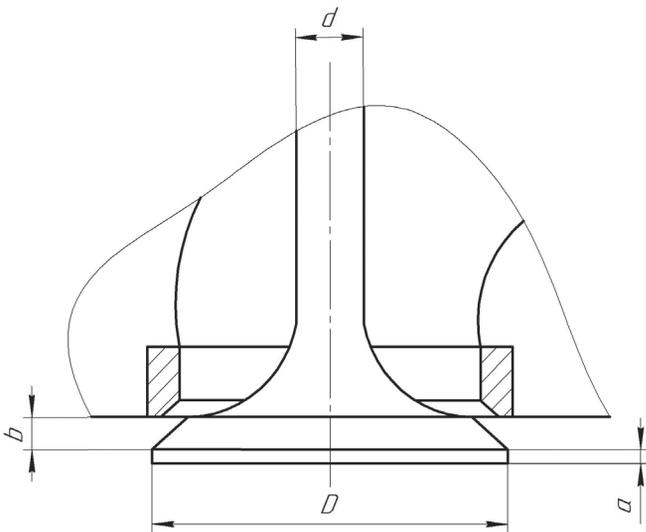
Схематическое изображение профиля рабочей части выпускного клапана: D – диаметр тарелки клапана; a – ширина цилиндрического пояса; b – ширина рабочей фаски; d – диаметр стержня
